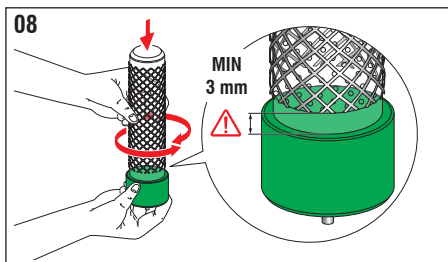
Riavvitare delicatamente il tubo ionizzante afferrandolo alla base (parte verde).
